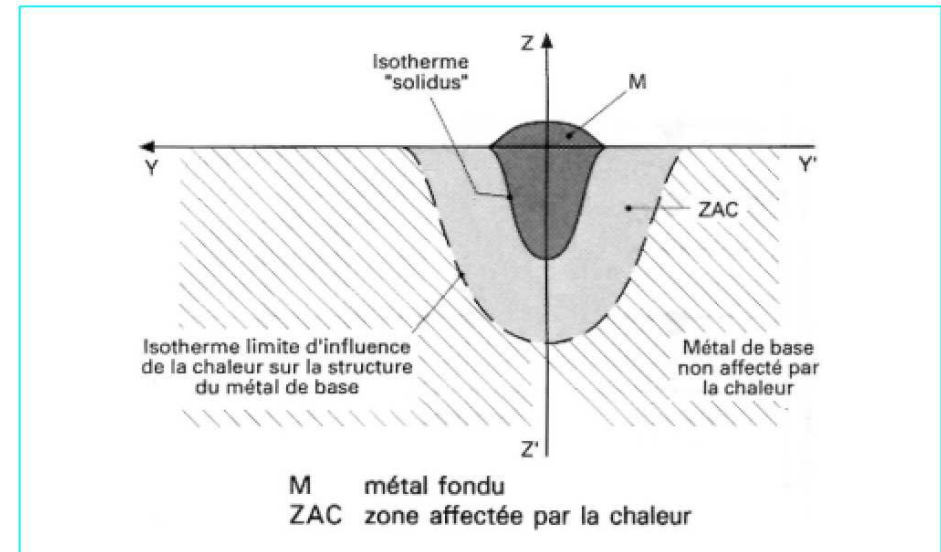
Définition des différentes zones d'un joint soudé
